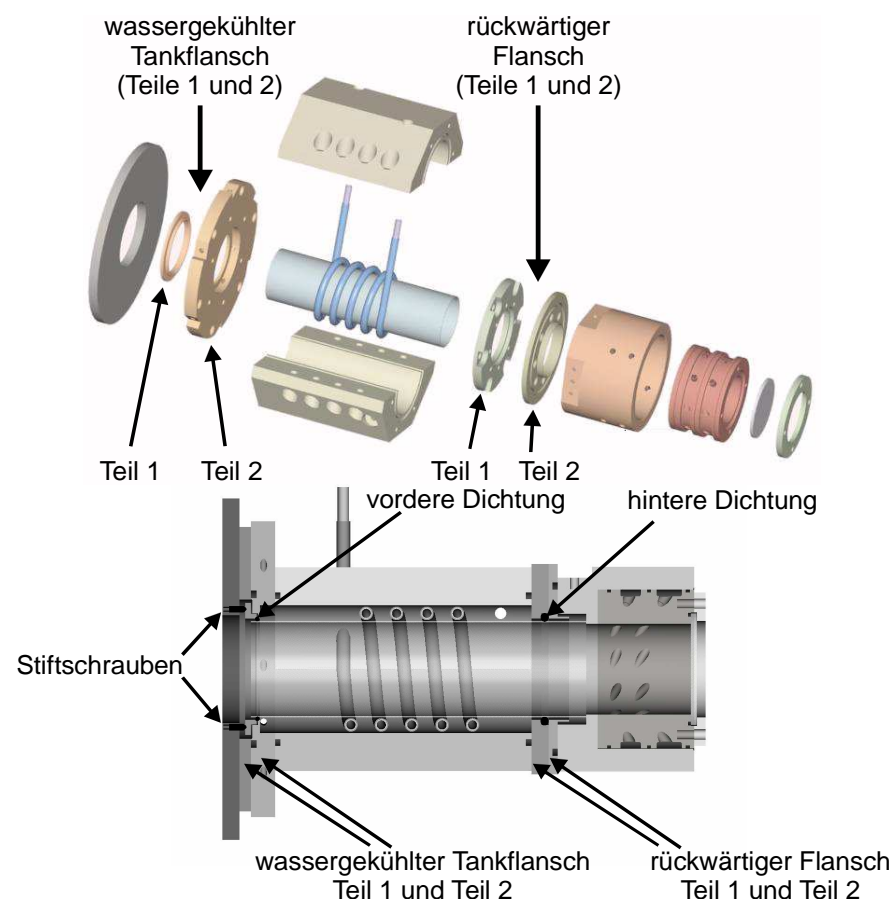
Explosions- und Schnittzeichnungen des IPG5
